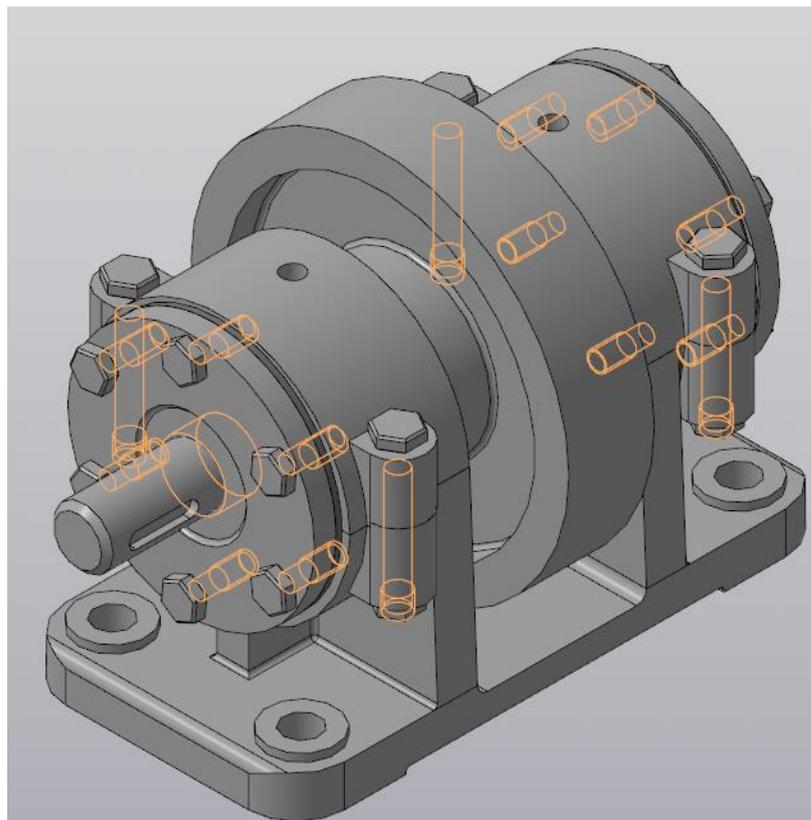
КЭМ сборки «Ролик поддерживающий»
